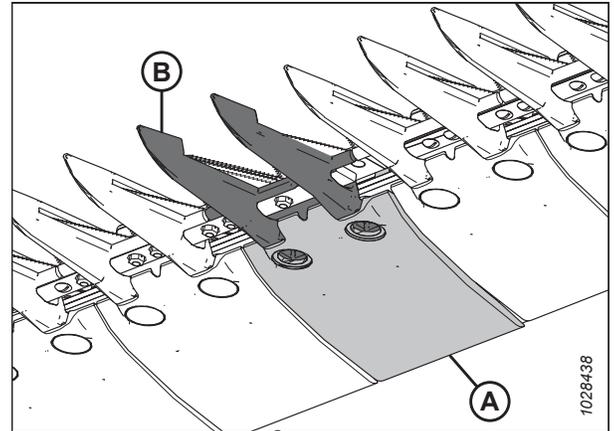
Doigt du couteau central pointu et plaque d'usure
